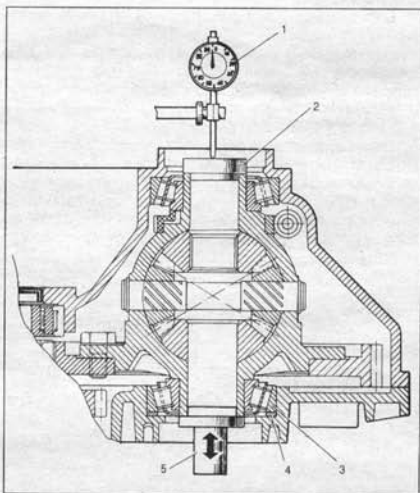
Схема подбора толщины регулировочного кольца подшипников дифференциала:
